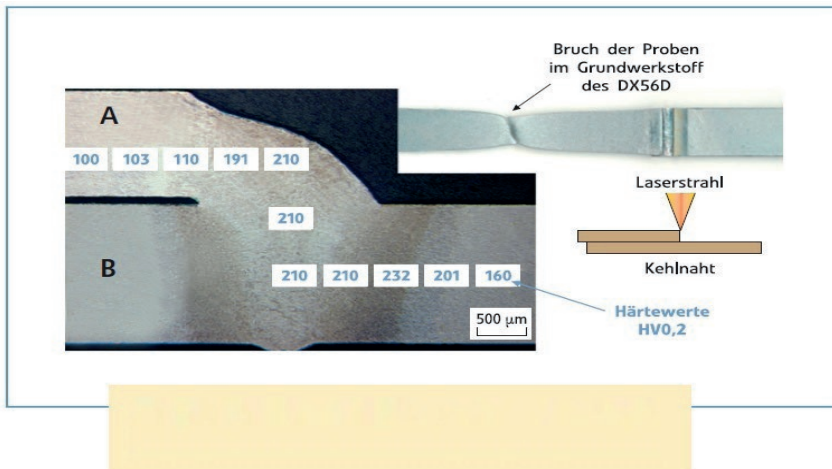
Зображення лазерного зварного шва з м'якої сталі глибокої витяжки DX56D (A) товщиною 1,5 мм і високоміцної сталі H420LAD (B) товщиною 2 мм
